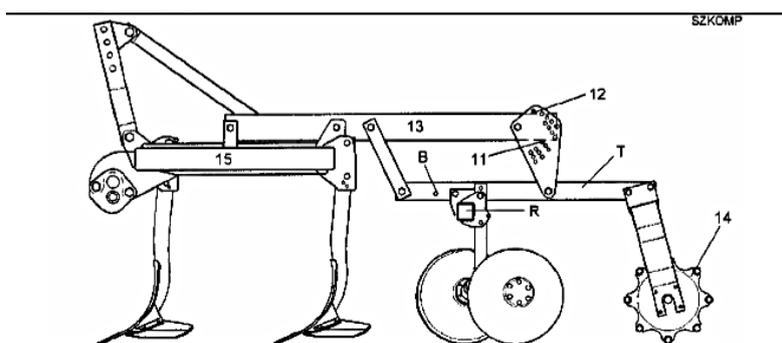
Регулировка трубчато-ребристых катков
